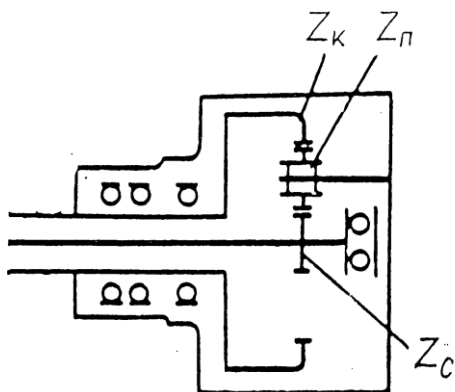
Схема конечной передачи (планетарного редуктора) тракторов К-701 и Т-150К
